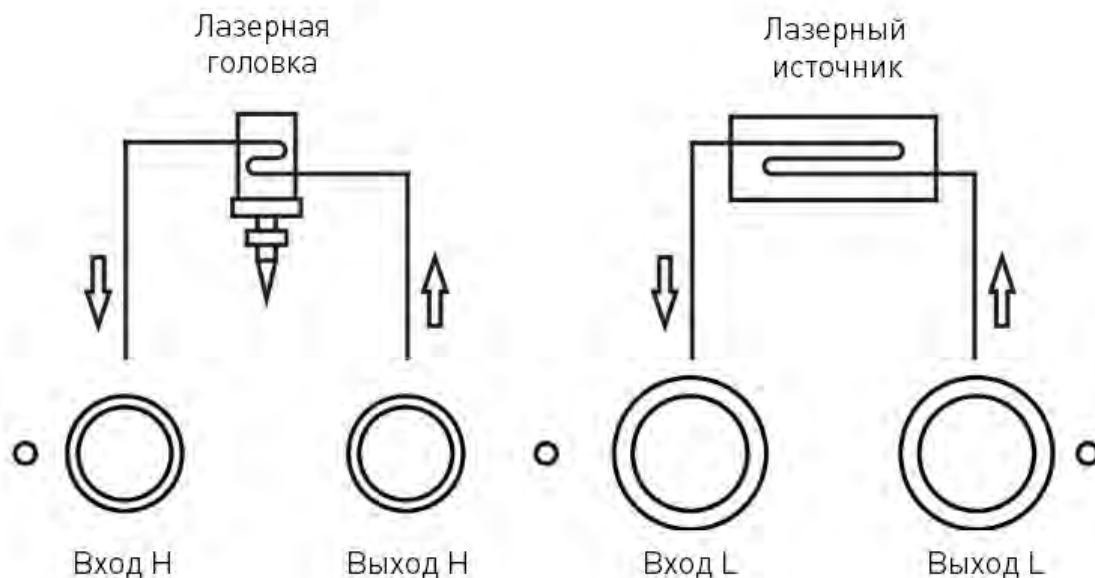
Способ соединения чиллера и лазерного станка.
